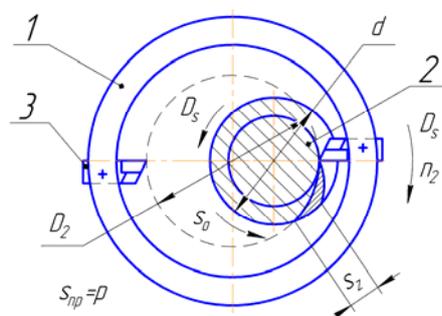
Схема вихревого нарезания резьбы: 1 – вихревая головка; 2 – нарезаемый ходовой винт; 3 – фасонный стержневой резец; D – диаметр головки; d – диаметр нарезаемого винта; s_0 – круговая подача, мм/зуб; s_{np} – продольная подача, мм/об
